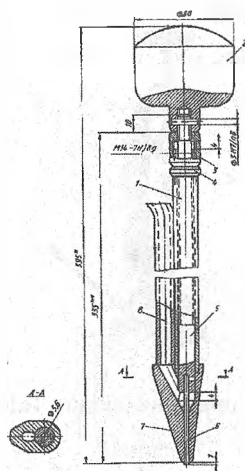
Приспособление для забивания гвоздей в каблук
